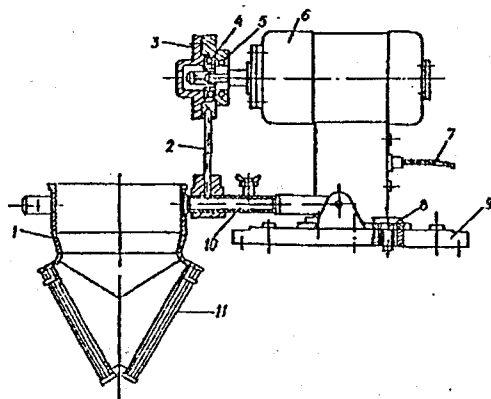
Вібросито СО-3А: 1 - корпус з обіймою; 2 - шатун; 3 - головка шатуна; 4 - кулькопідчіпники; 5 - ексцентрикова муфта; 6 - електродвигун; 7 - кабель; 8 - гвинт; 9 - плита; 10 - кронштейн; 11 - сито
